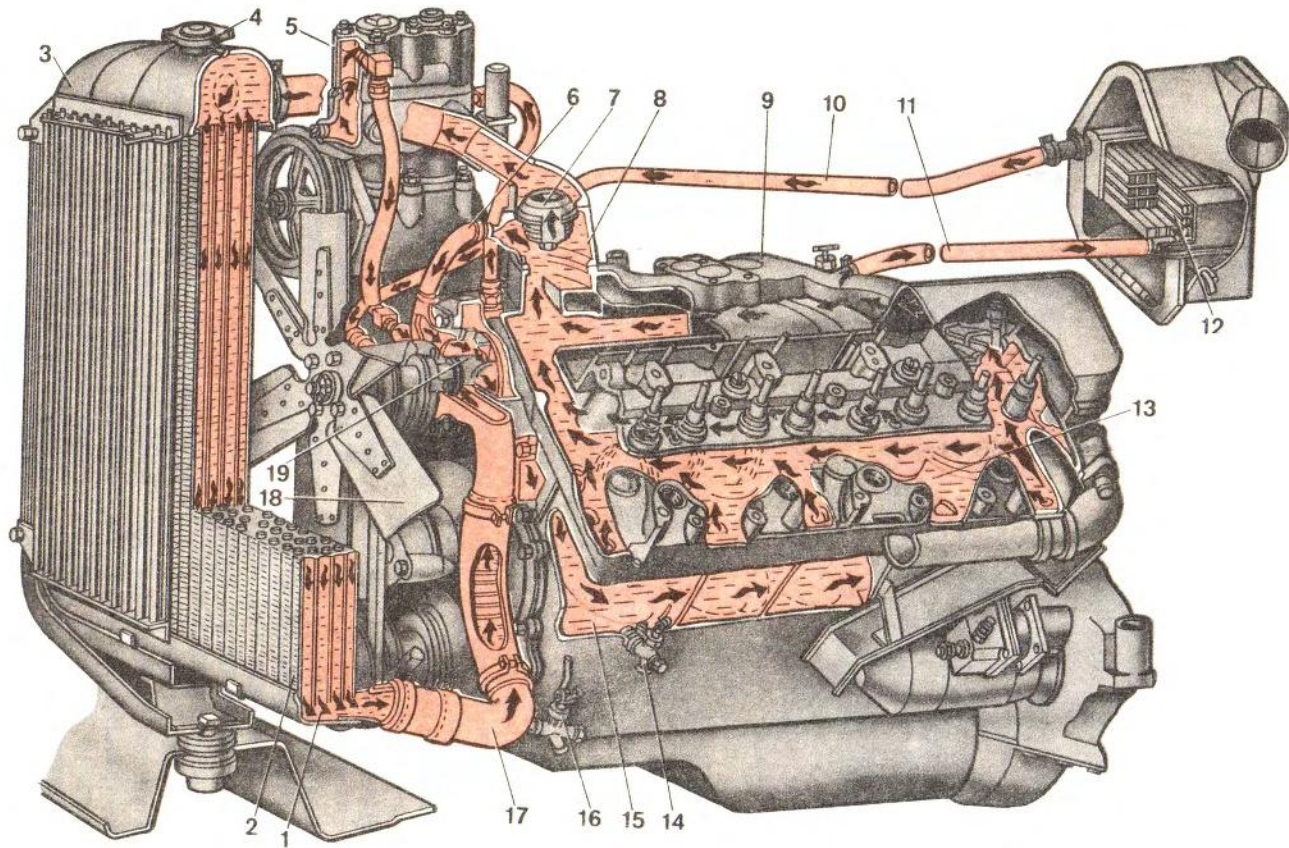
Схема охлаждения двигателя ЗИЛ-130:
